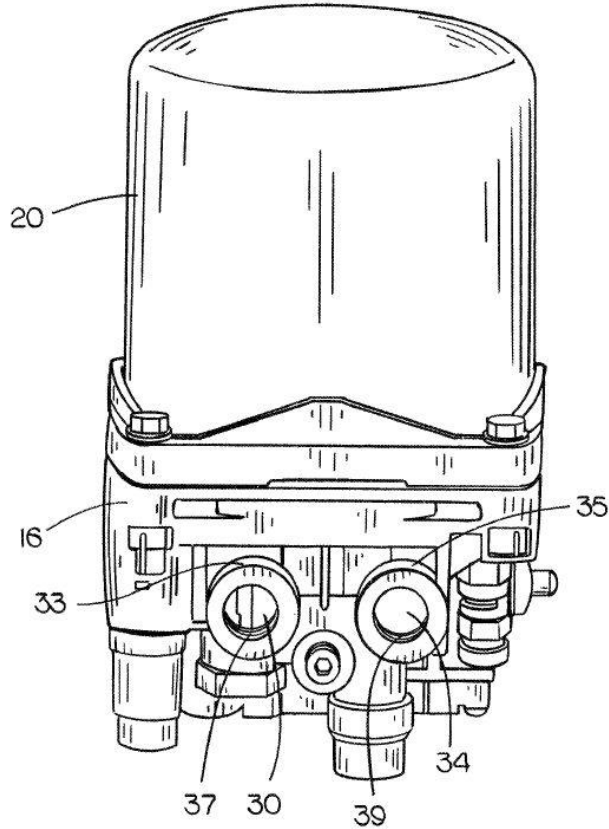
Hava kurutucuların manifold sistemi ile montajlanması
